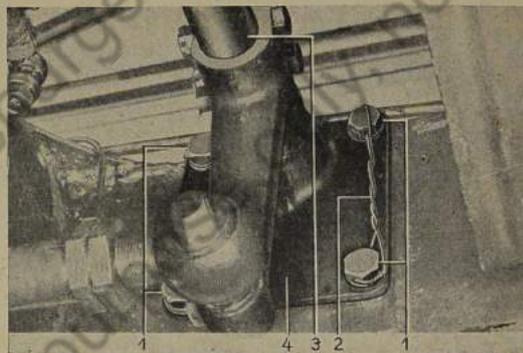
Rechten Lagerbock für Lenkzwischenwelle abschrauben
